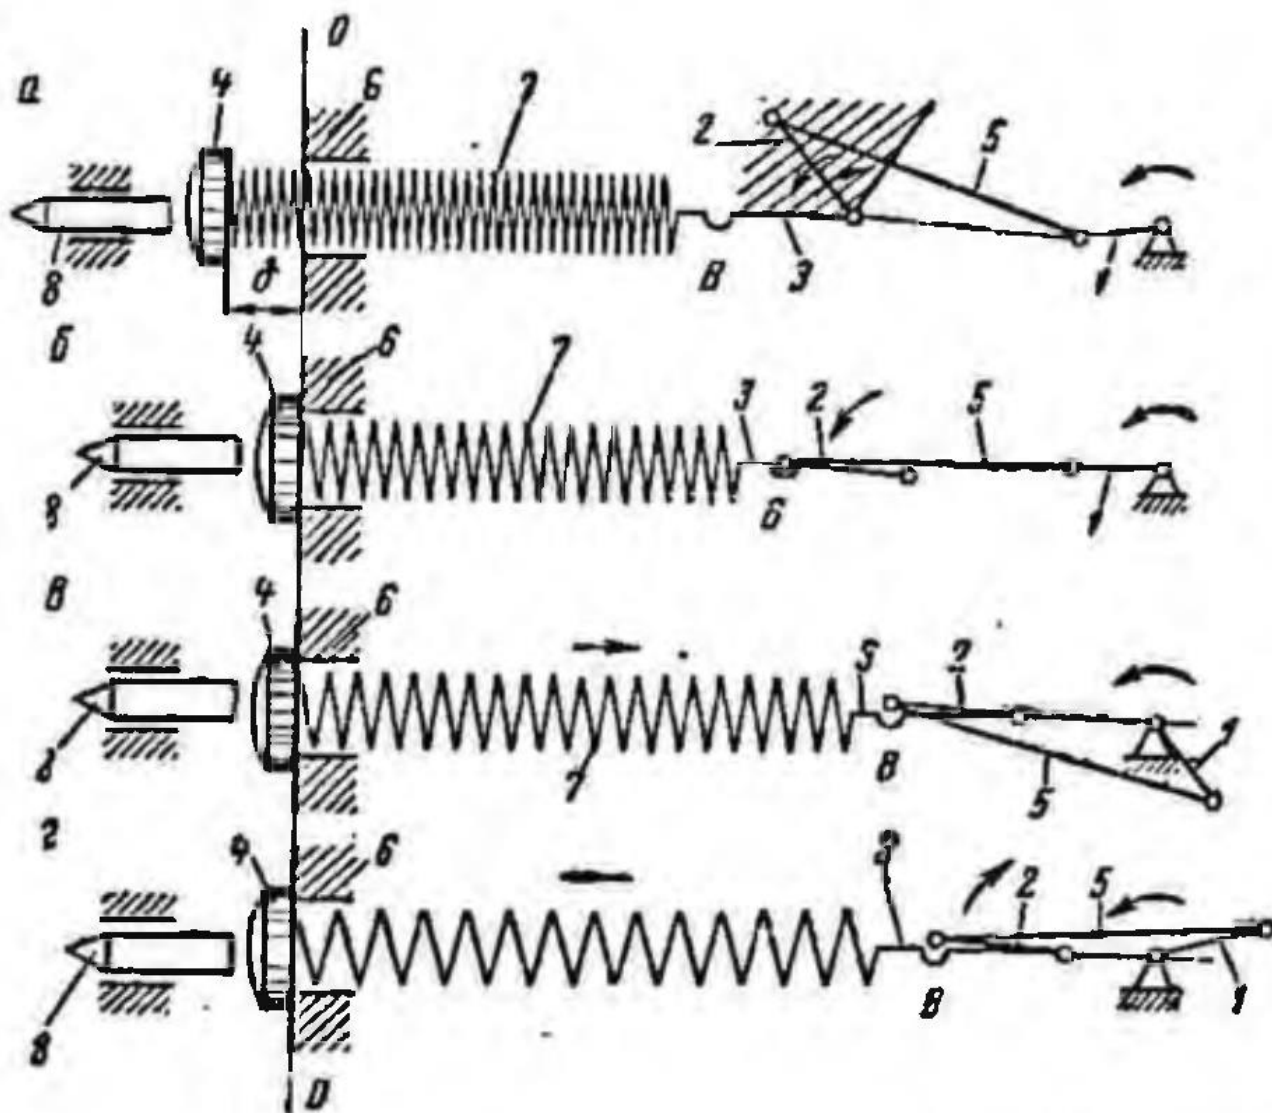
Схема шарнірного захоплюючого механізму з пружним бойком (пружиною): а - холостий хід; б-захоплення пружини; в- робочий хід; г - закінчення робочого ходу
